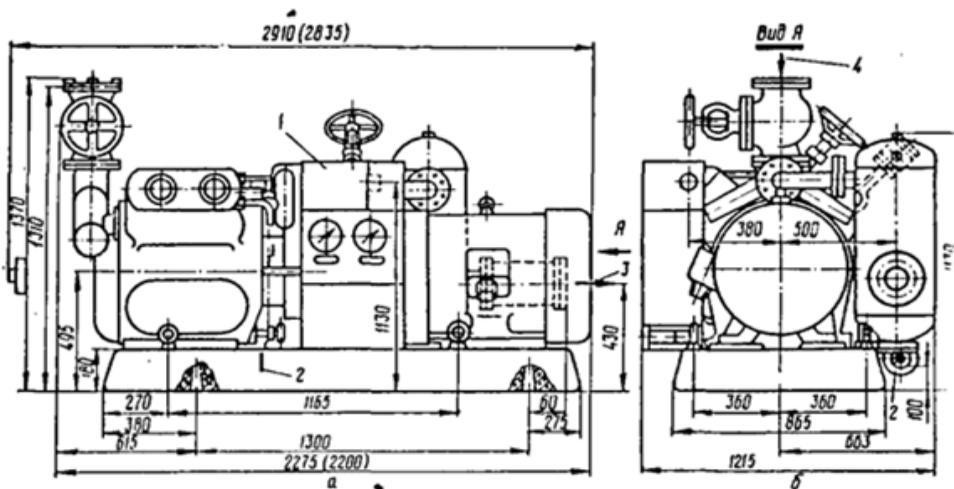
Внешний вид и размеры компрессорного агрегата А 110-7-01: а – вид сбоку; б – вид спереди. 1 – блок приборов; вентиль для заправки масла; D, 65 – линия нагнетания; D, 100 – линия всасывания.
